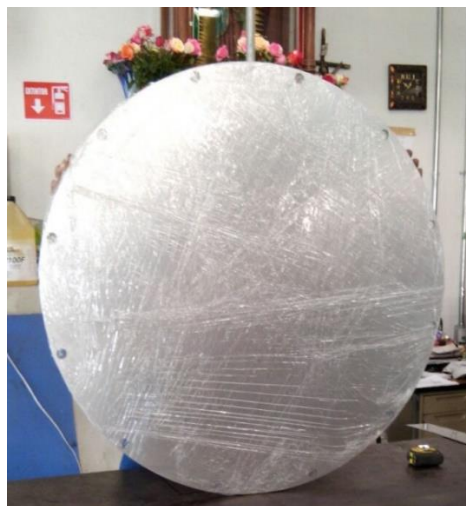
Muestra la fabricación de la tapa superior del cuerpo principal de la Boya, la cual es de la placa de Aluminio 6061 T6 de 1/2" para su fabricación.
